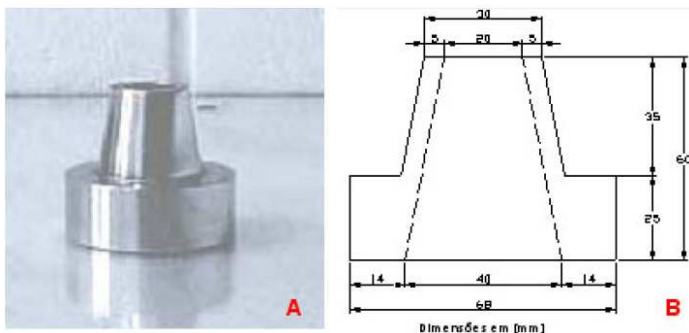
Ensaio do Cilindro Espanhol (MARTINS, 2009)
